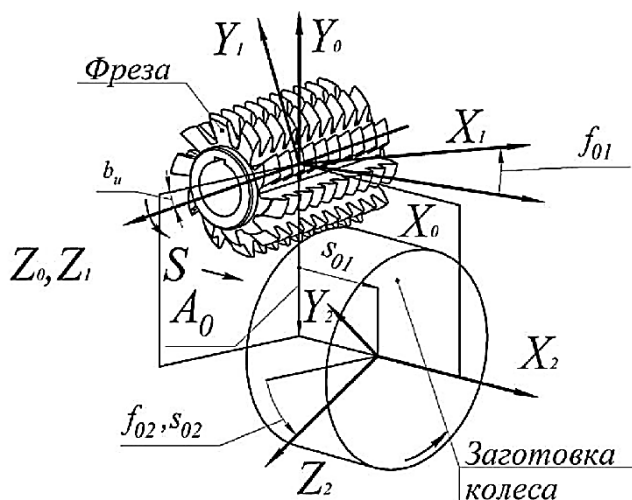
Розрахункова схема формоутворення косозубих зубчастих коліс черв'ячними фрезами
